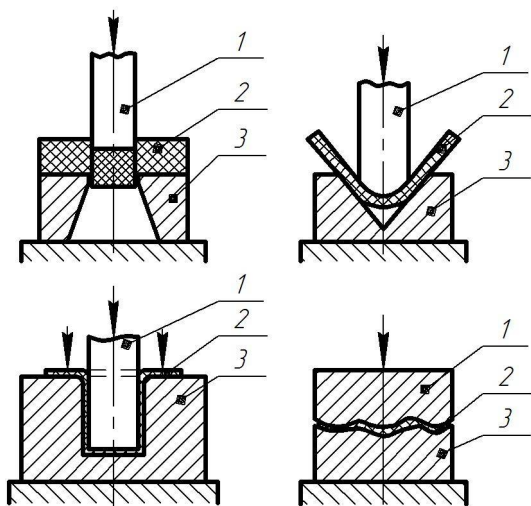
Етапи листового штампування: 1 – пуансон; 2 – заготівка; 3 – матриця
